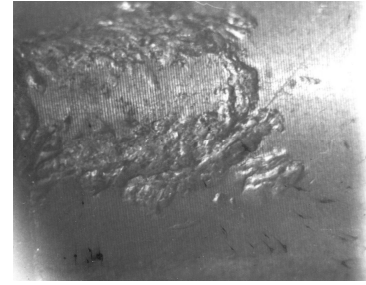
Вид усталостного разрушения поверхностного слоя вкладыша
